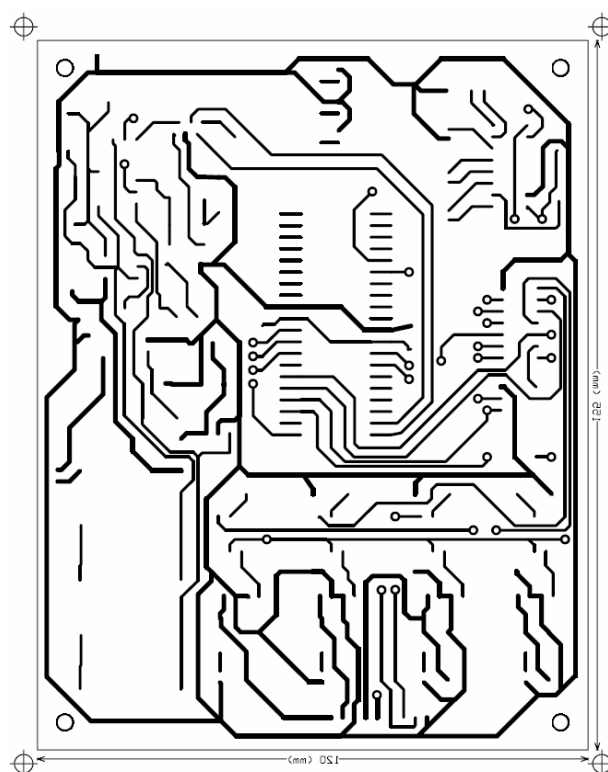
Layout de la cara inferior del PCB con efecto espejo.
